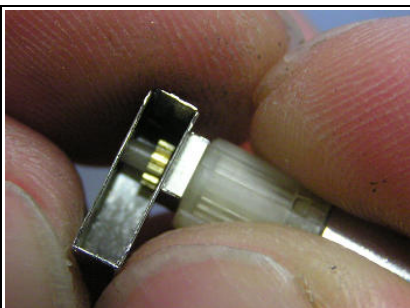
Das Zahnrad soll wie abgebildet ohne Abstand in das Gehäuse ragen. Noch nicht kleben oder löten!
